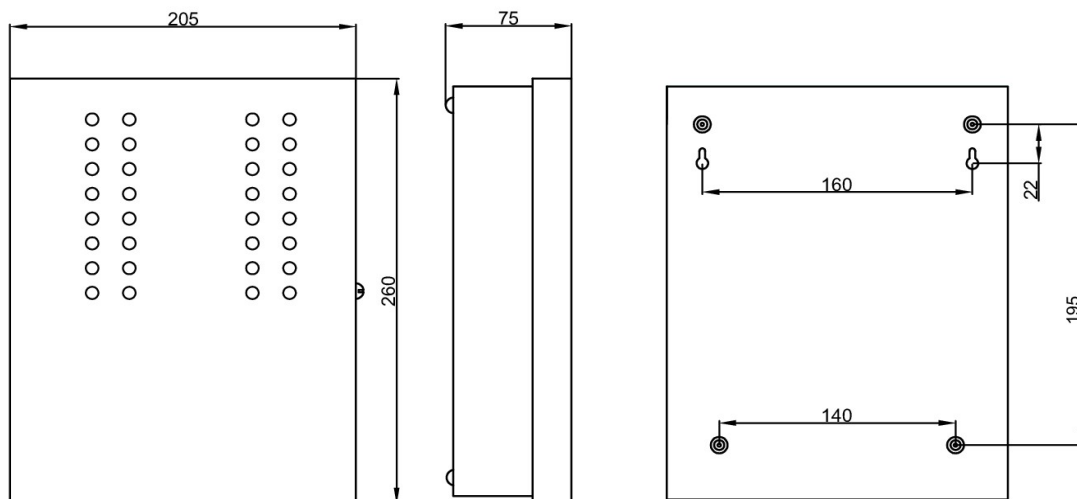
Габаритные и установочные размеры прибора, металлический корпус
